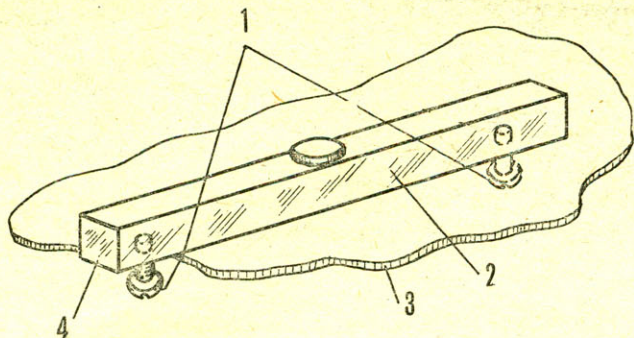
Крепление к матрице закладной детали для формования полости под плавник:
